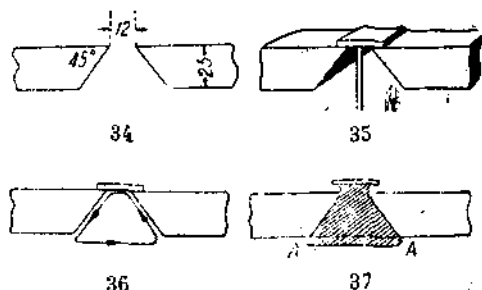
37. Способ потолочной дуговой сварки.
